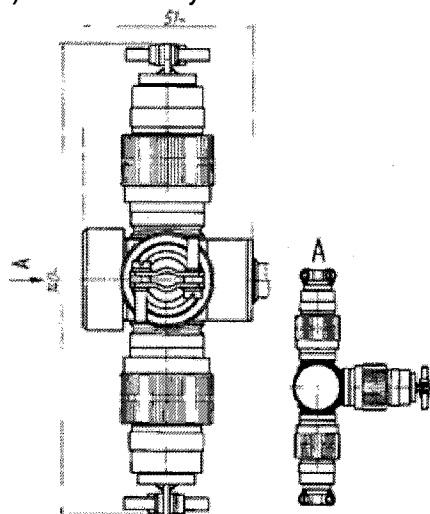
Кресленик зовнішньої частини ТСП-1390 з головкою БАУИ.408724.023 СБ
